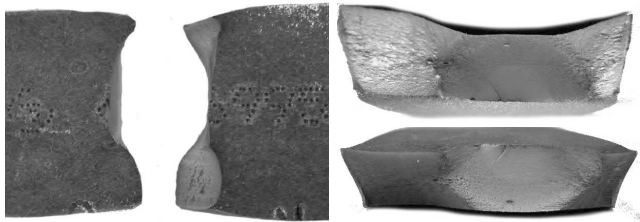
Bruchbild (links) und Bruchflächen (rechts) der mittels Nadelmarkierung markierten Stahlprobe 460v-15-Na-01
